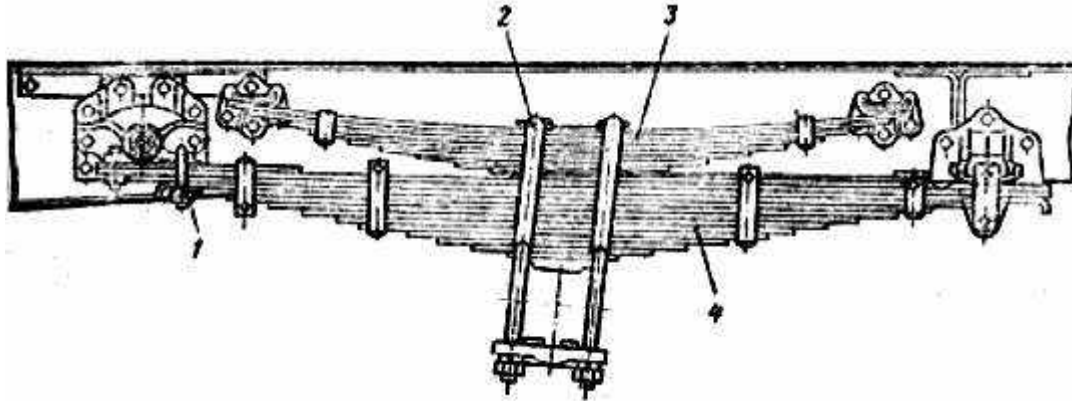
Конструкція ресори з підресорником: 1 – стрем'янка вушка ресори; 2 – стрем'янка ресори; 3 – підресорник; 4 – ресора.
